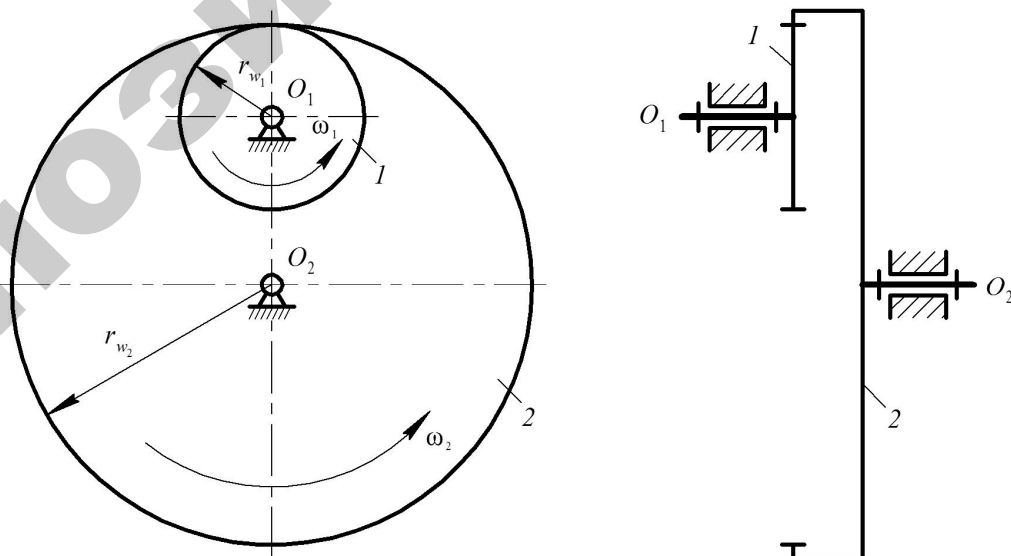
Схема зубчатой передачи с внутренним зацеплением колес
